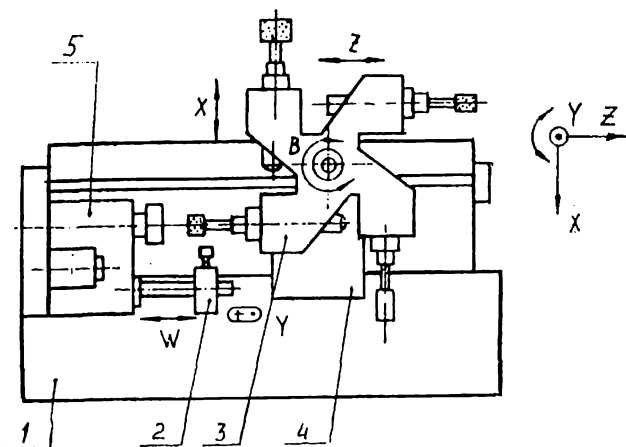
Схема шліфувального верстата з чотирьохпозиційною revolverною головкою:
